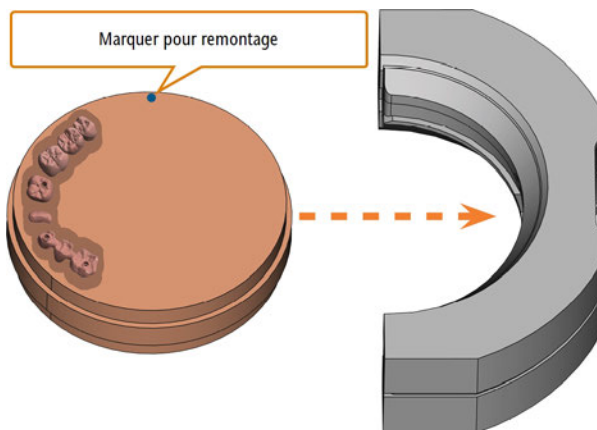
SERRER UN DISQUE DÉJÀ TRAITÉ AU SUPPORT DE PIÈCES BRUTES (MARQUES BLEUES POUR UN SERRAGE PLUS SÉCURITAIRE)
